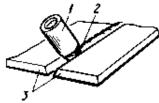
Схема контактно-экструзионной сварки пластмасс: 1- экструдер; 2 — мундштук экструдера; 3 — свариваемые летали.
